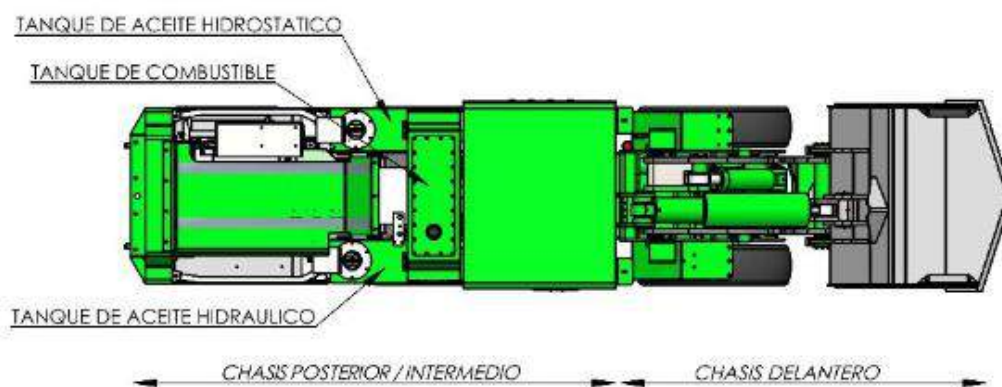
Componentes principales del Mini Loader XLH05D – vista de planta
